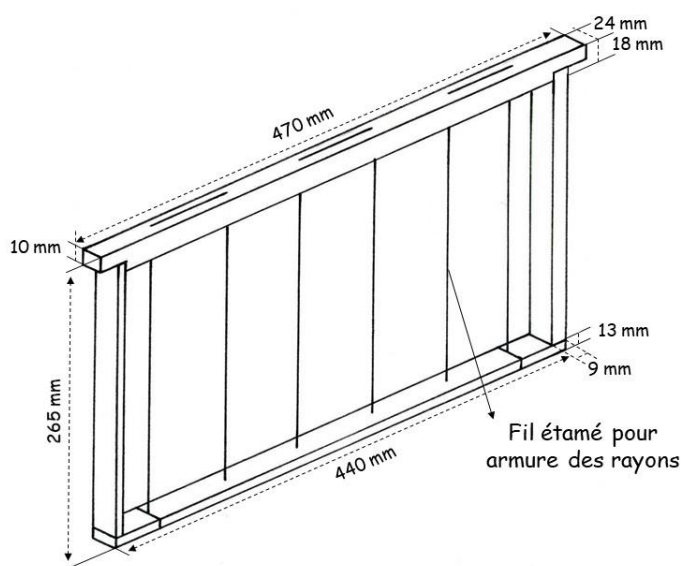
Plan de cadre en bois pour ruche rectangulaire, avec armure en fil de fer étamé.
